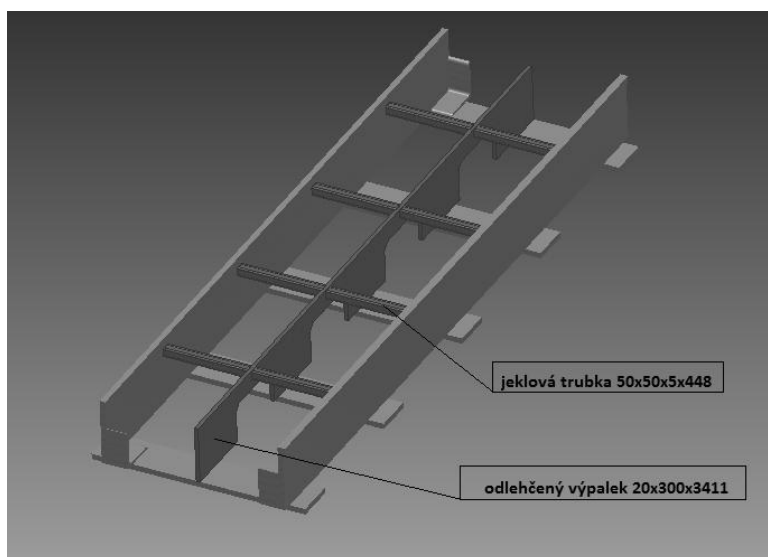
Pohled na druhou inovovanou konstrukci kolejí
